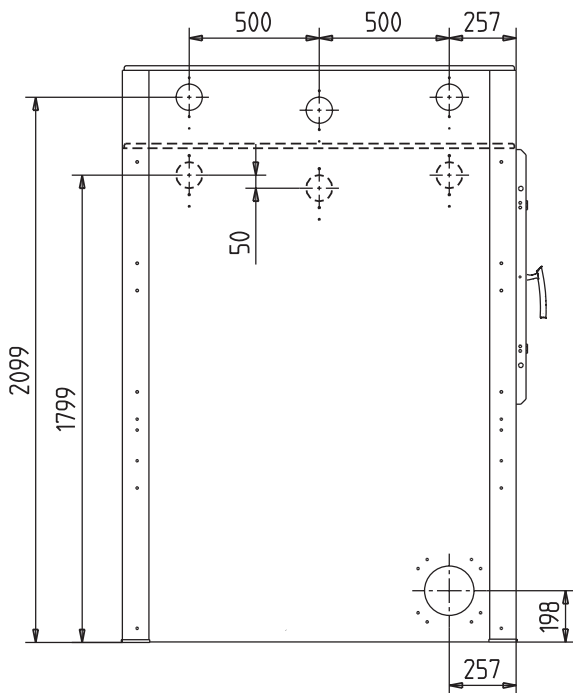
Stahlblech-Tanks mit Breite 1,5 m
